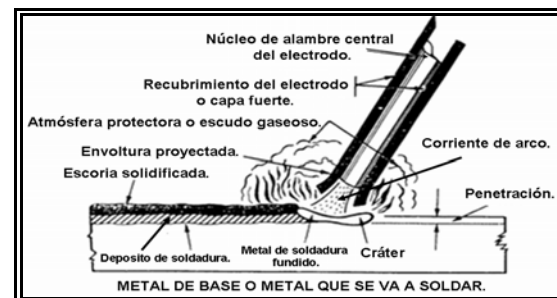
Proceso de soldadura por arco eléctrico
